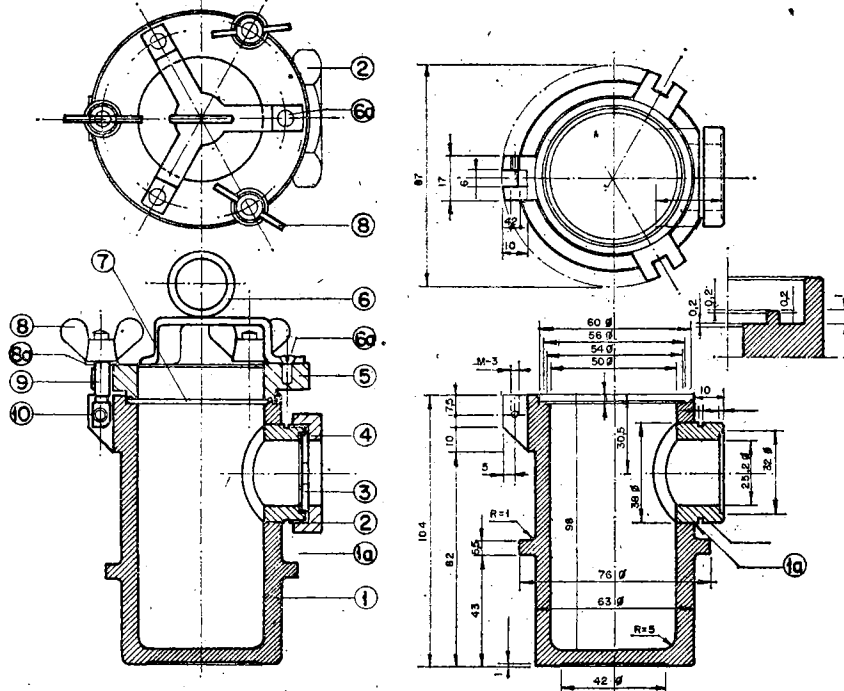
= Recipiente a presión montado vistas esquemáticas en sección vertical y en planta
